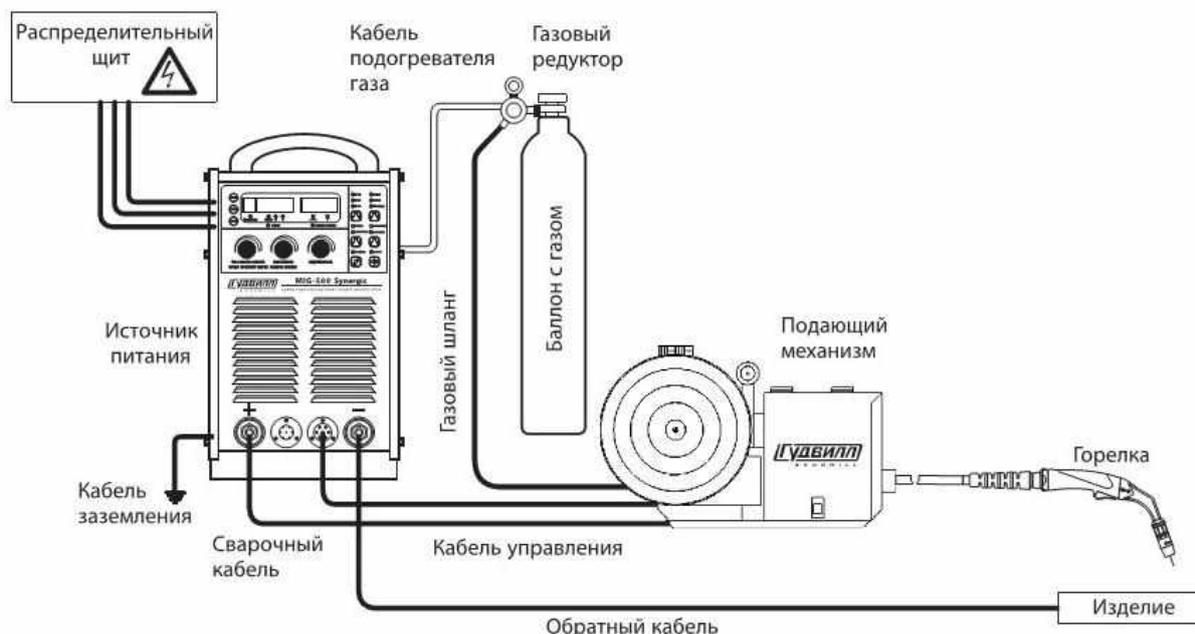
Комплект сварочного оборудования для MIG/MAG сварки
